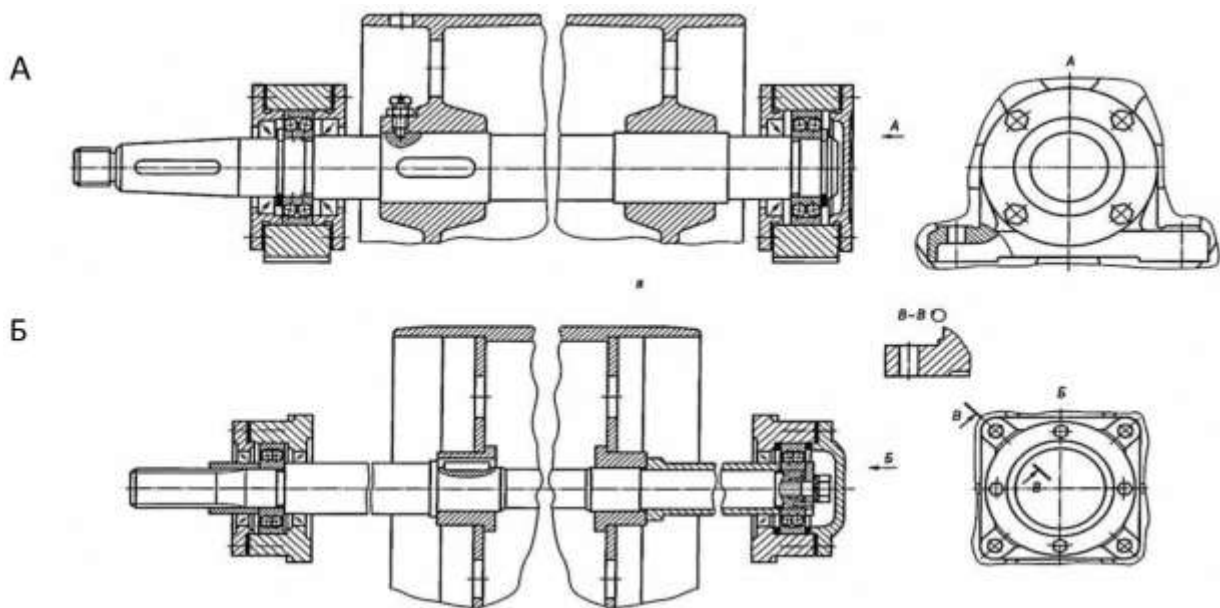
Конвеєрні приводні барабани змонтовані на валу: А – вилитий; Б - зварений
